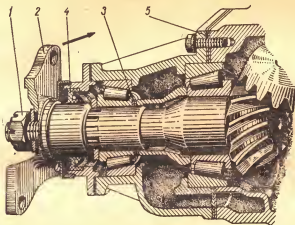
Проверка затяжки подшипников вала ведущей шестерни автомобиля ЗИЛ:
